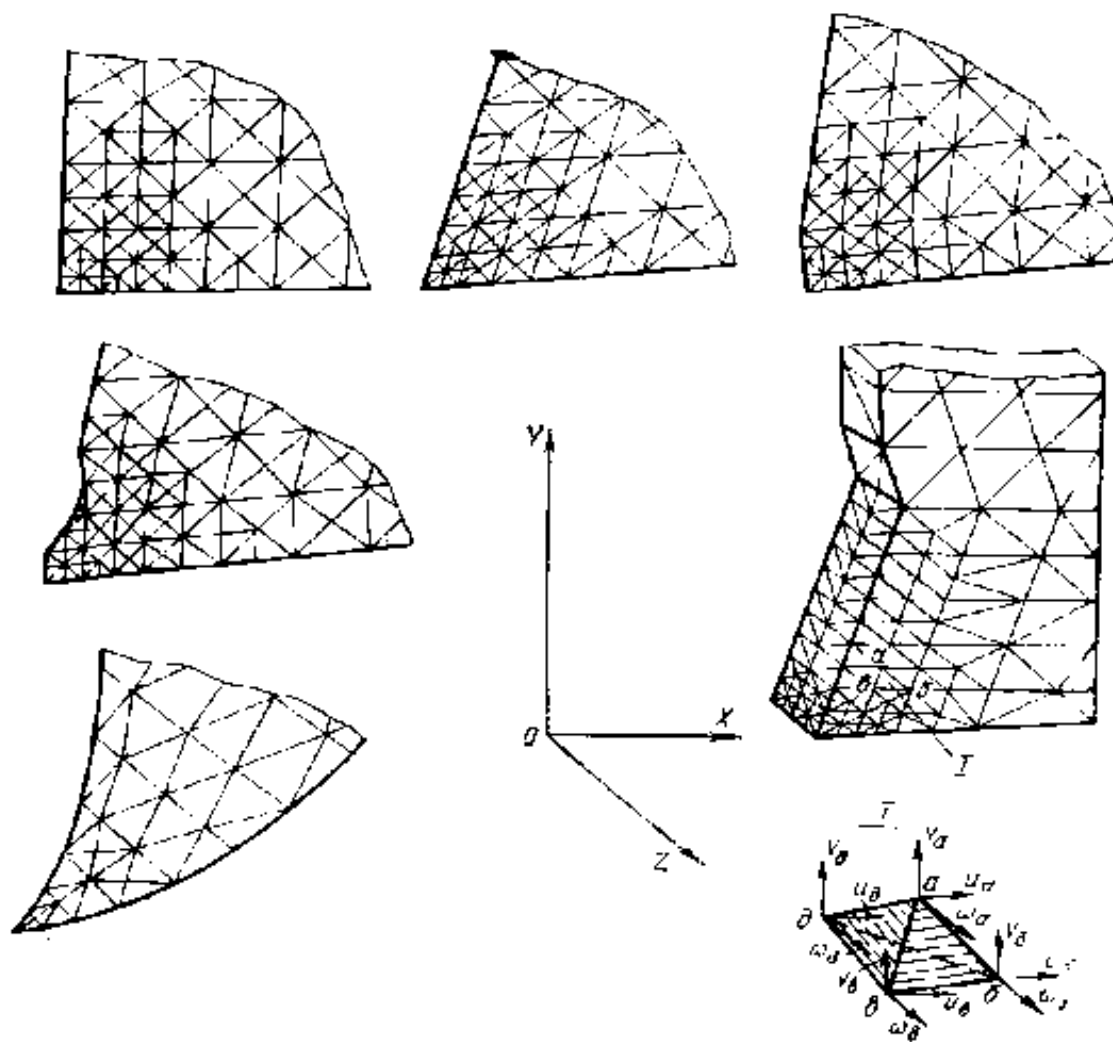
Схемы разбивки режущей части инструмента [72]
